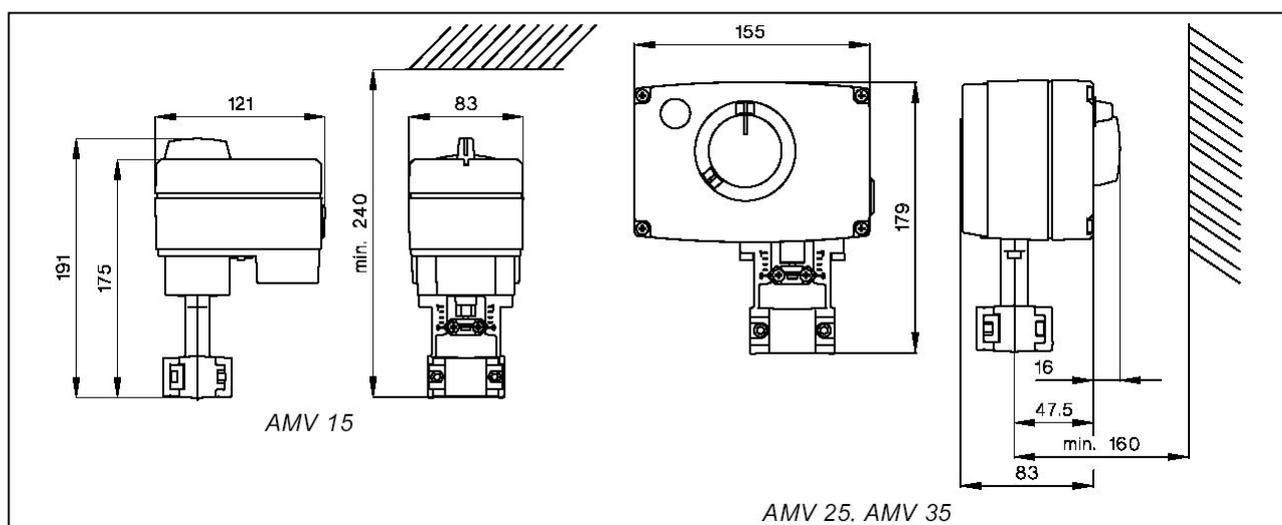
Габаритные и присоединительные размеры AMV 15, 25, 35.
